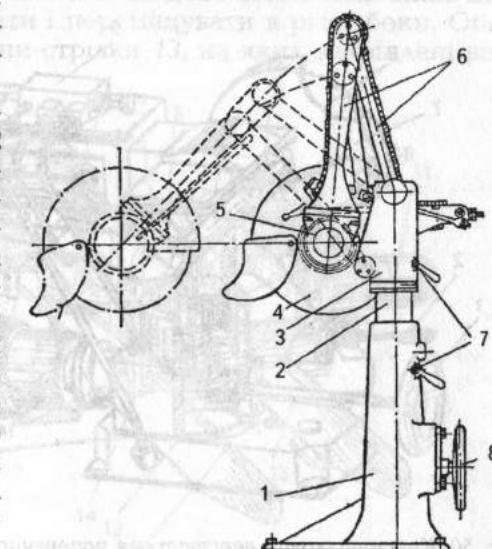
Круглопилковий маятниковий верстат ЦМЕ-2:
